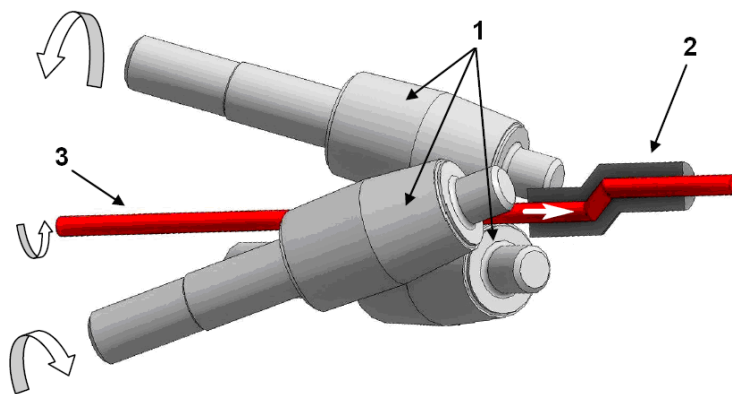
Схема совмещенного процесса «винтовая прокатка-РКУ прессование» (1 – конические валки; 2 – ступенчатая РКУ матрица; 3 – заготовка)
